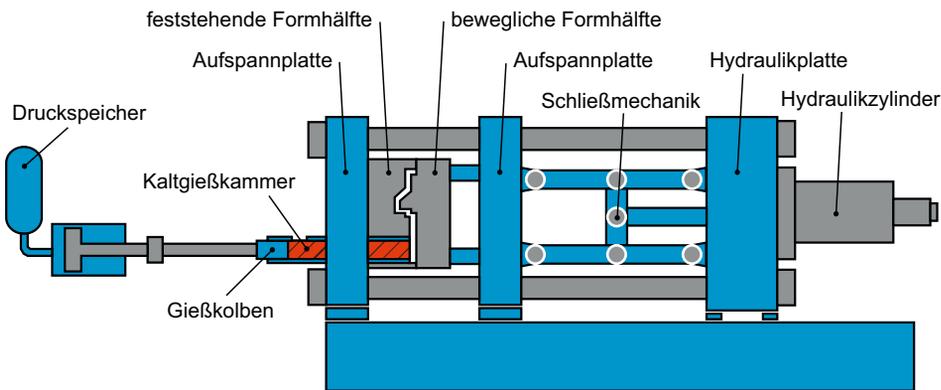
Druckgießmaschine mit horizontaler Befüllkammer
